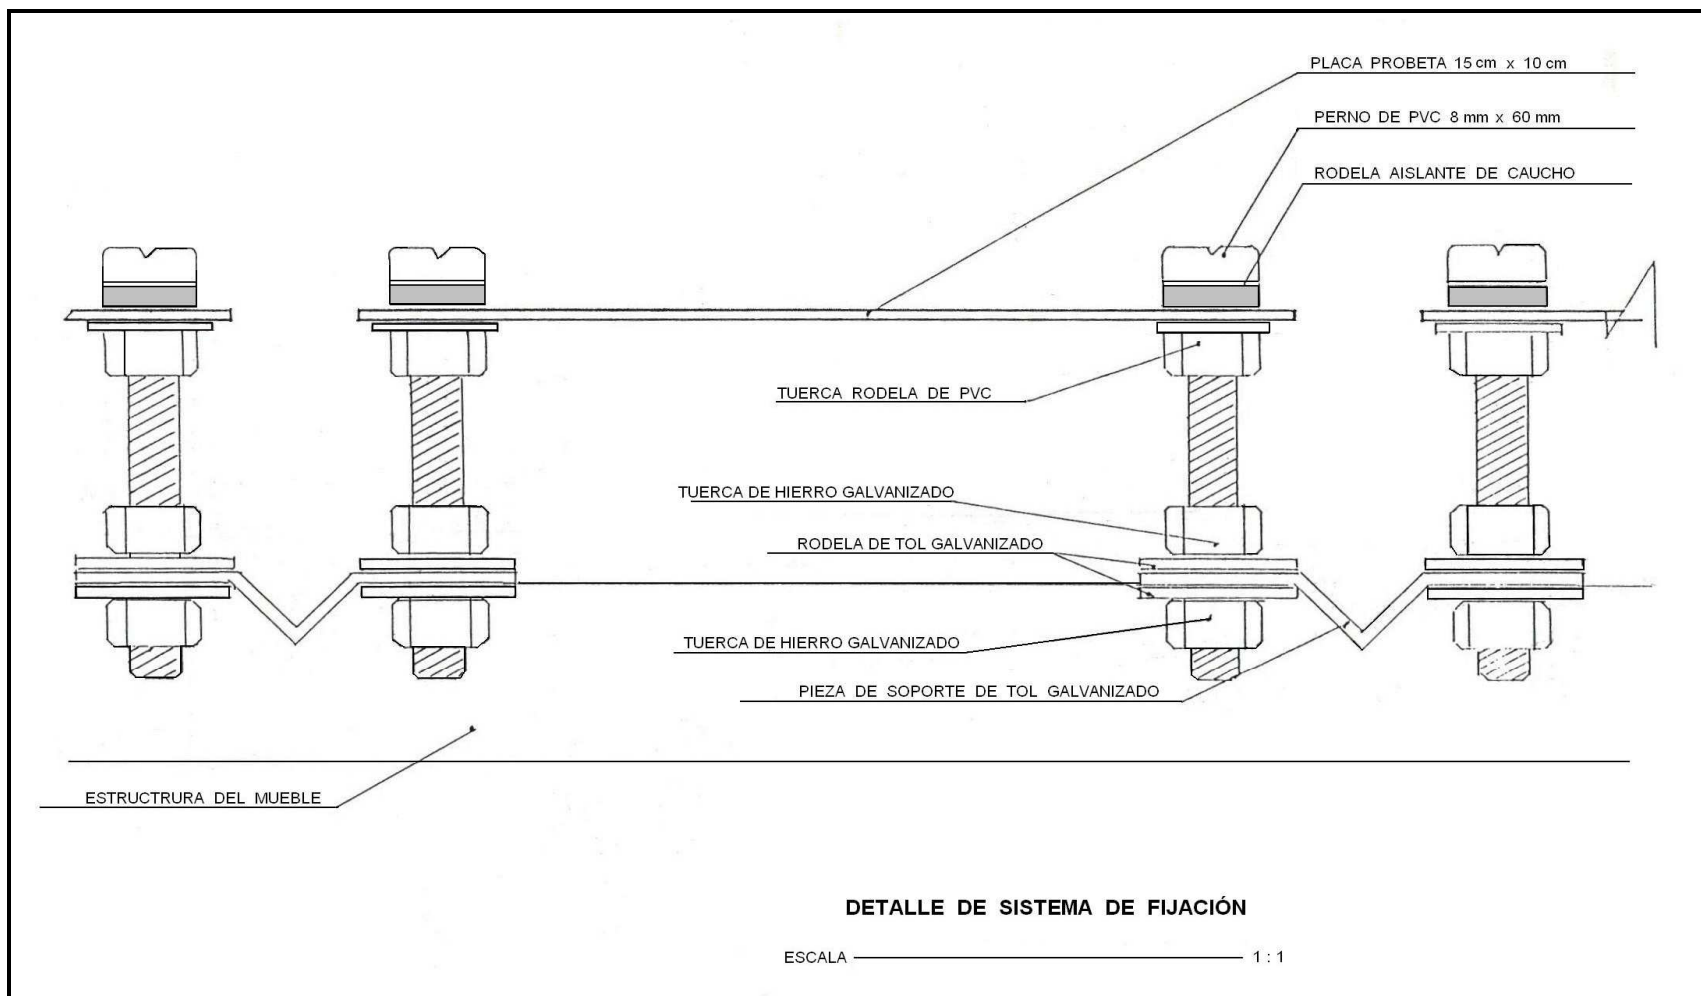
Detalle del Sistema de Fijación<sup>2</sup>
